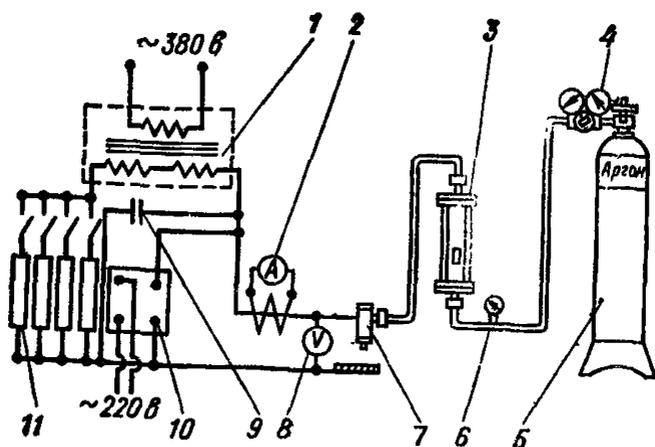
Схема поста сварки неплавящимся электродом
